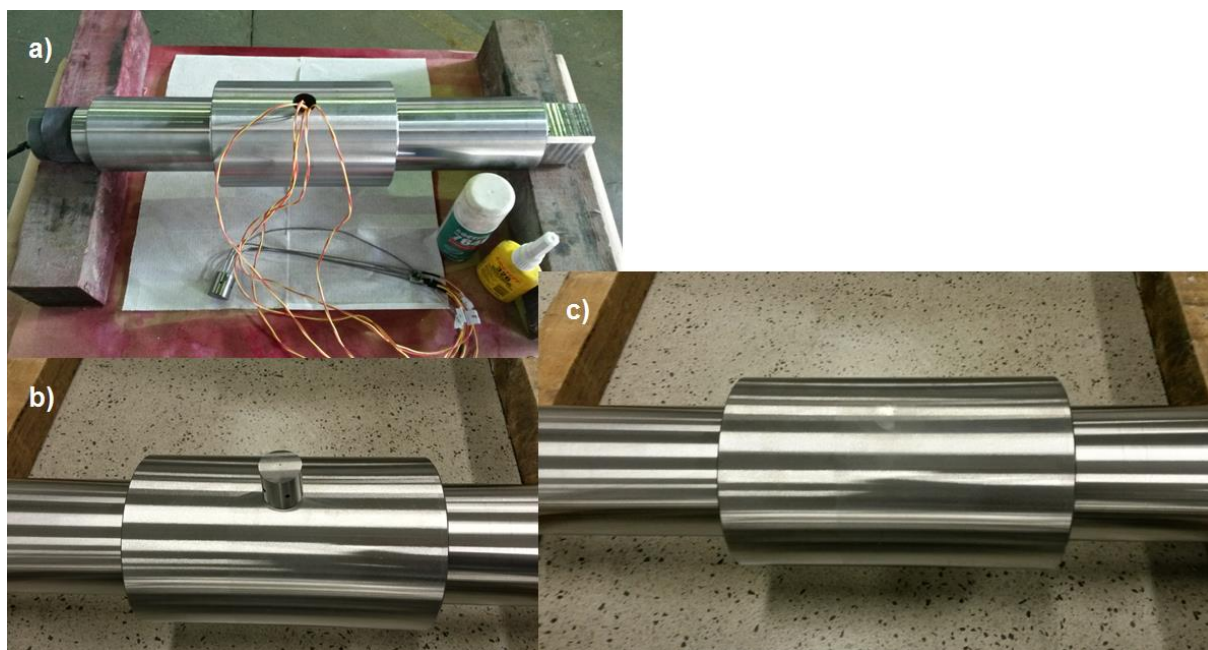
Etapas de montagem do inserto instrumentado: a) passagem dos cabos de extensão; b) encaixe do inserto após aplicação de cola para fixação; c) fechamento.
